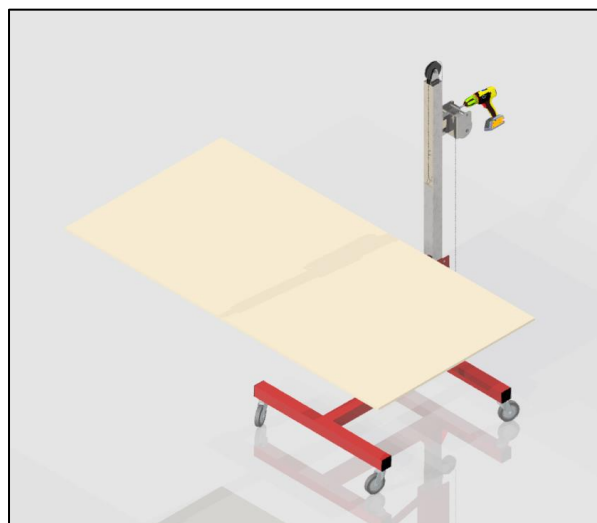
Plancha de gypsum colocada sobre la plataforma.
